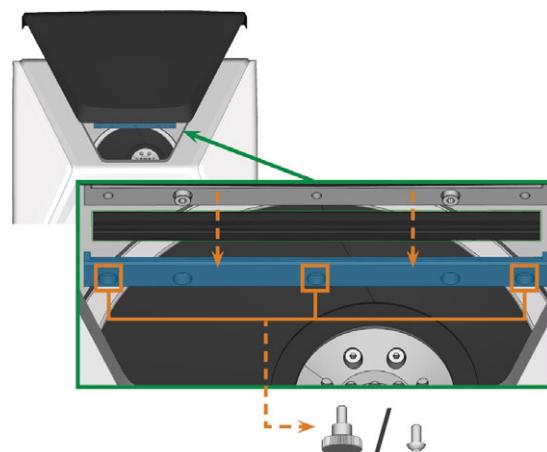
RETIREZ L'ESSUYEUR DE LA MACHINE
